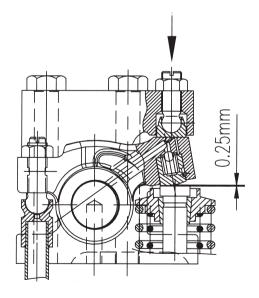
冷态排气门端气门间隙0.25mm Fig. 3 End Valve Clearance of Cold-State Exhaust Valve 0.25mm
